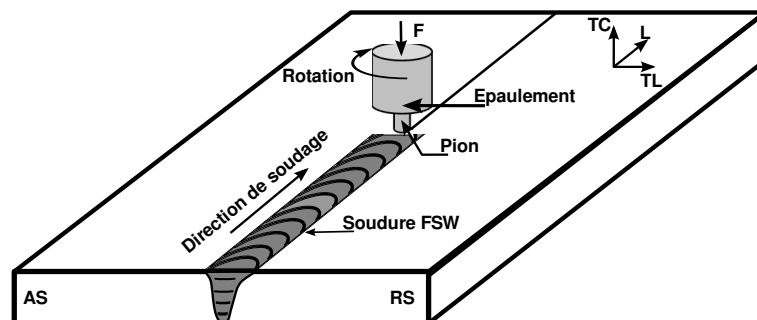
Paramètres du procédé de soudage par FSW
